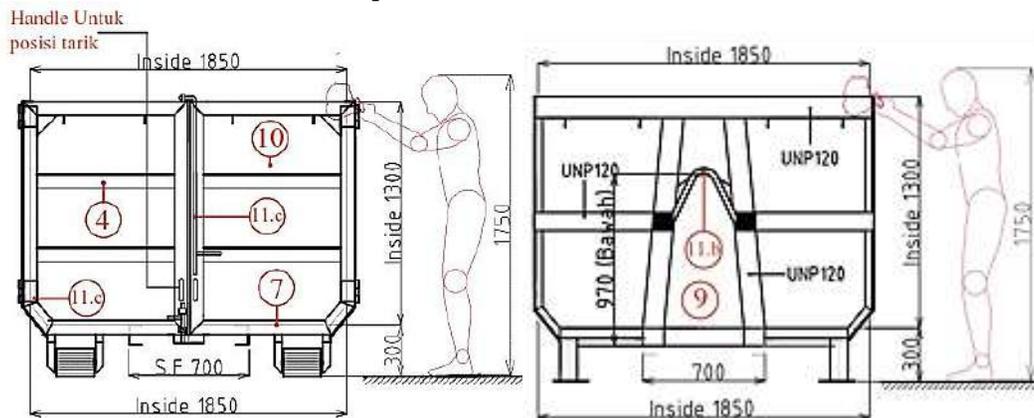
Tampak Samping Kontainer Terbuka Dimensi 8m³
